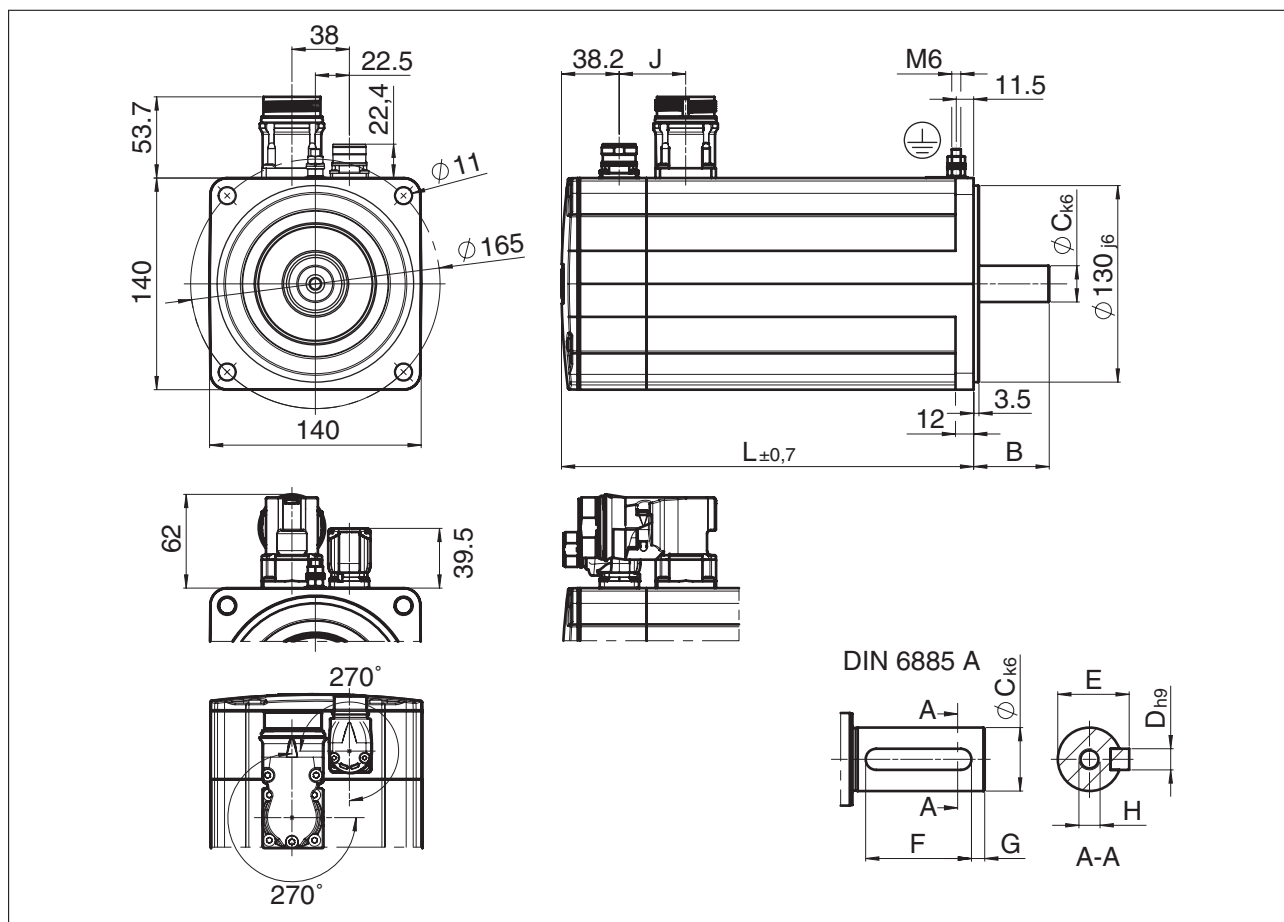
Dimensioni BSH1402 (T); BSH1403 (T); BSH1404 (P)
